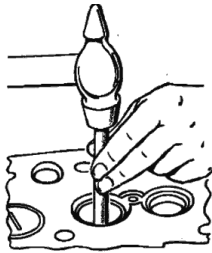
Выпрессовка направляющей втулки стержня клапана
